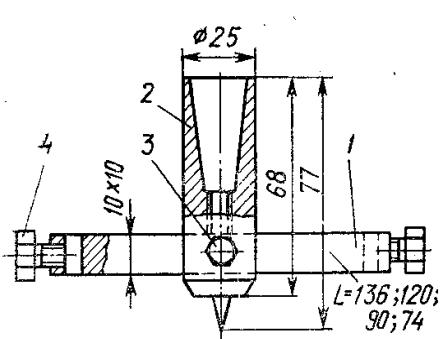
Приспособление для выборки резонаторных отверстий в деках:
